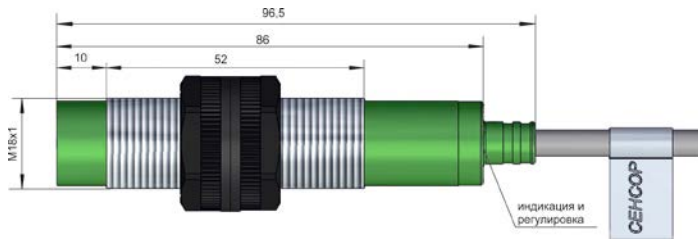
Габаритные размеры ВБЕ-Ц18-82В...
